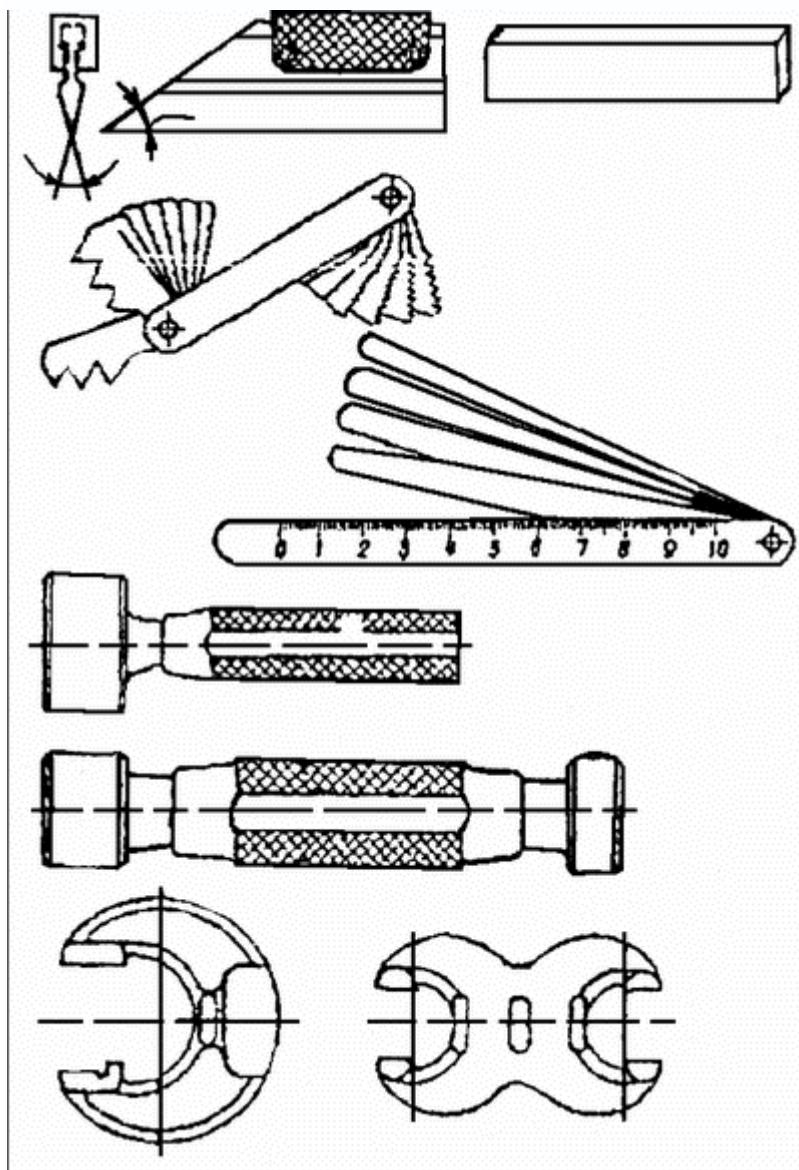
Простые специальные инструменты для контроля размеров: а – линейка угловая с двухсторонним скосом; б – линейка прямоугольная; в – шаблон резьбовой; г – щуп; д – пробка сборная односторонняя; е – пробка сборная двухсторонняя предельная; ж – скоба предельная односторонняя; з – скоба предельная двухсторонняя
